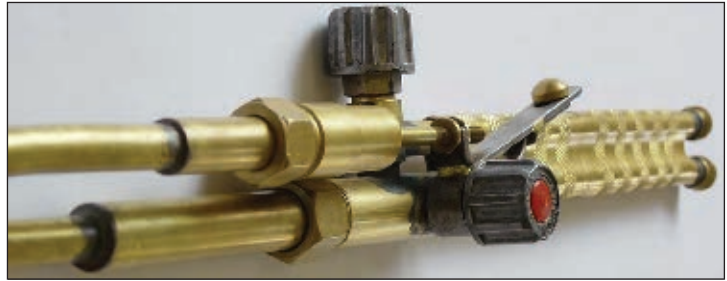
Резак для выплавки дефектов на поковках РПКЗ
